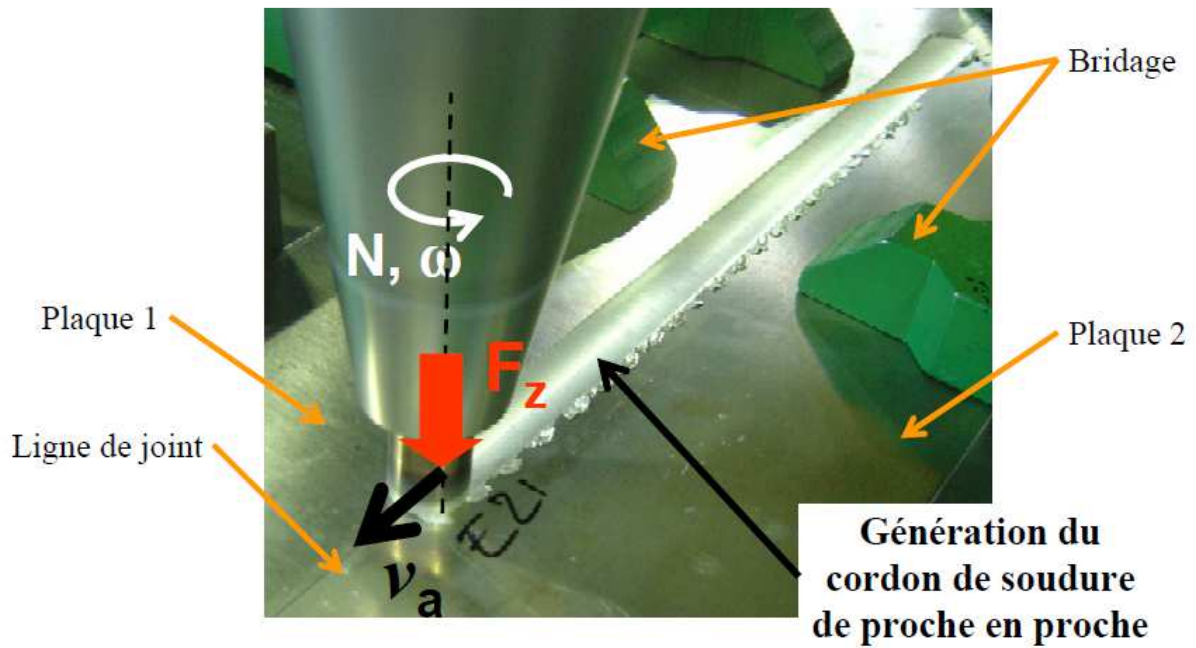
Génération du cordon de soudure de proche en proche.[3].
